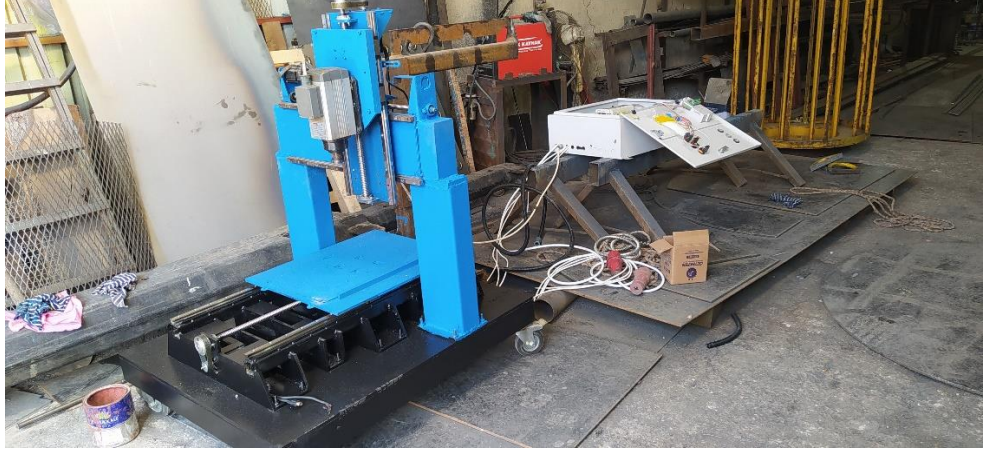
CNC Router Mekanik Kısım Son Montajı-1
